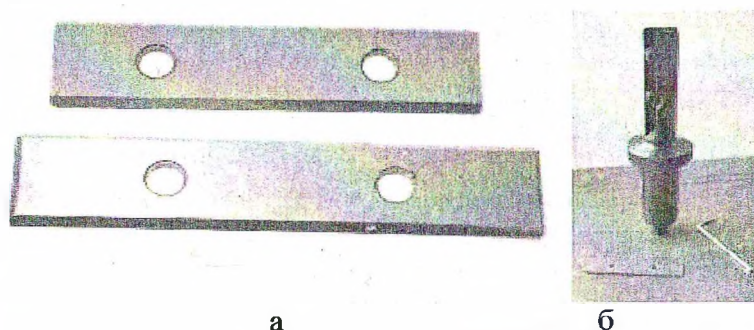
Пластинки фирм Leuco и Royce//Aug (а) и концевой фрезерный инструмент, оснащенный пластинками (б)
